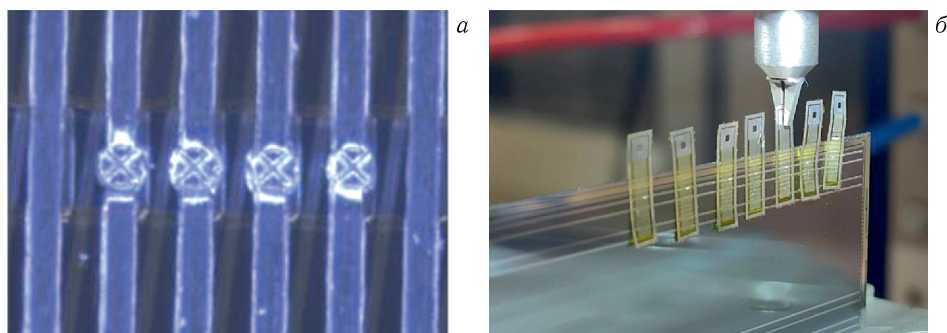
а) Кремниевый детектор с тестовыми образцами на установке для отрыва; б) ультразвуковая сварка четырех проводников по технологии ЛАС
